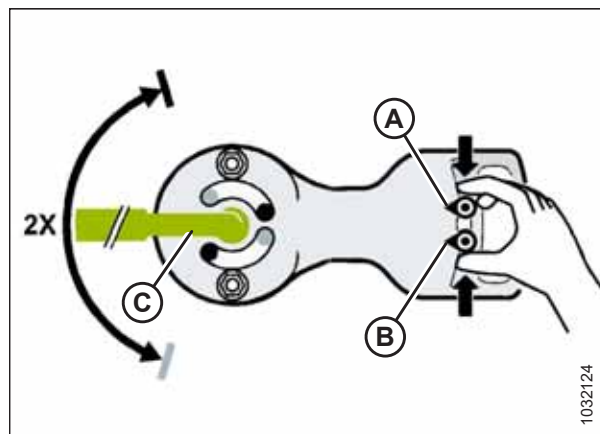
Ajustement de l'équilibrage des ailes — côté gauche illustré
